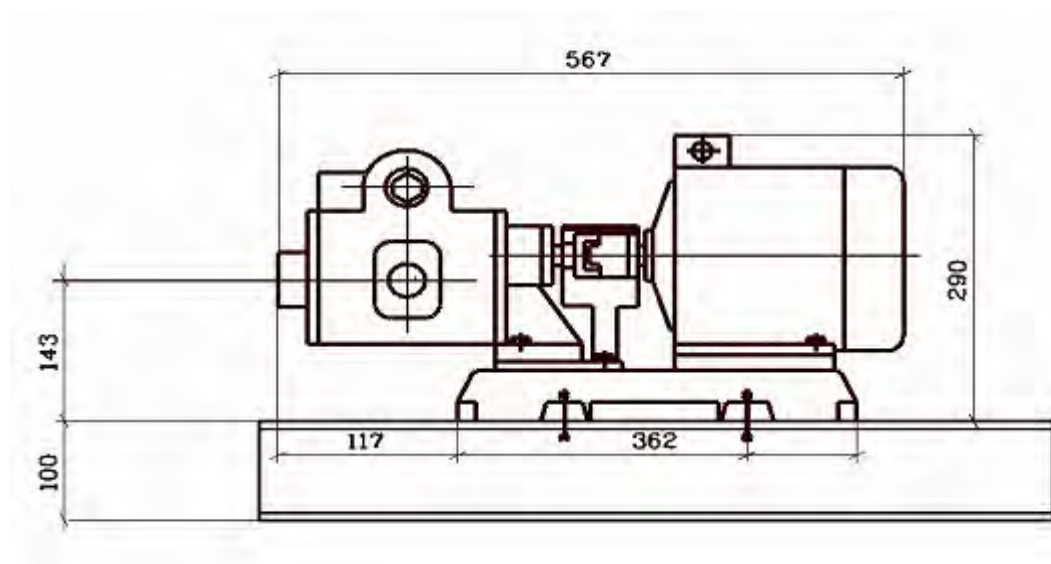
Габаритный чертеж насоса MVU20AP001, MVU30AP001
